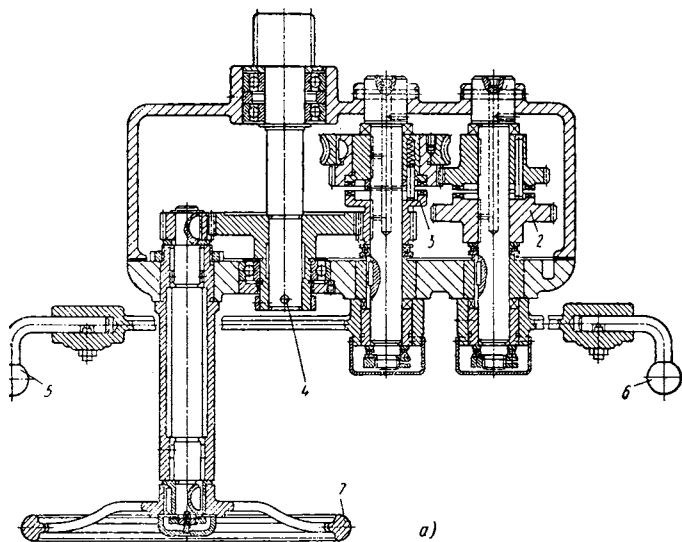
Развертка фартука поперечного суппорта станка 1П365
